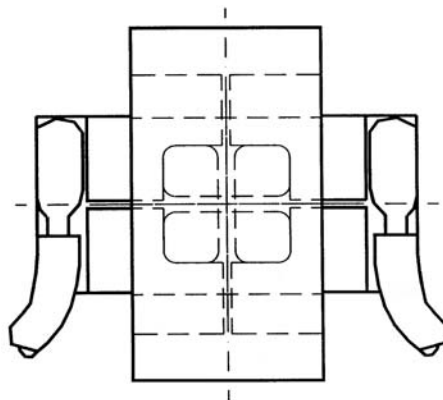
Die Chipabmessungen wurden so gewählt, dass sich die elektrischen Anschlüsse nicht gegenseitig behindern.
